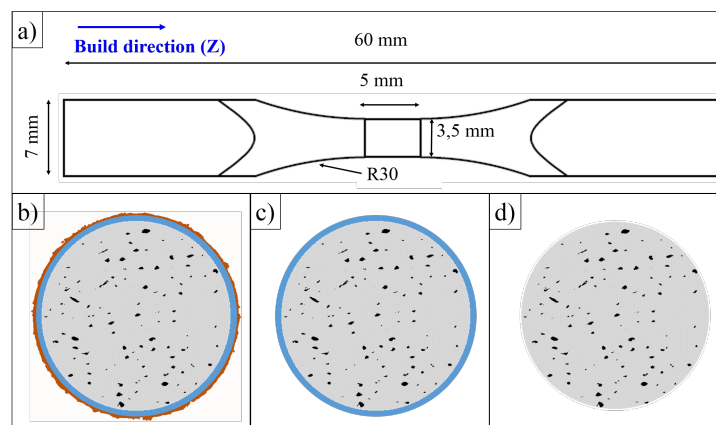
a) Géométrie des éprouvettes testées et vue en coupe de la section utile a) brute de fabrication b) après polissage de l'extrême surface d) après tournage pour enlever intégralement le contour.
